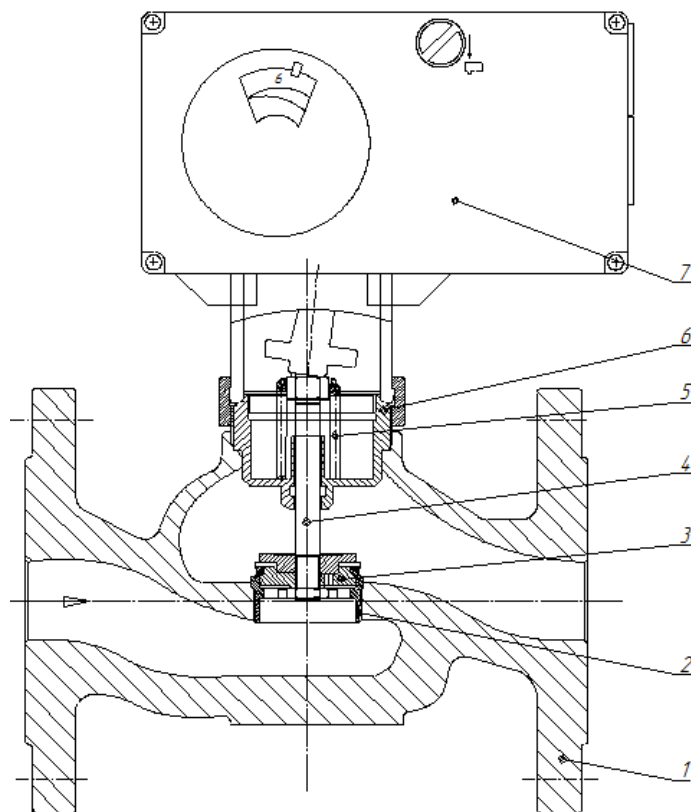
Загальний вид запропонованого електромеханічного водострумний змішувача: 1 – корпус; 2 – сідло клапана; 3 – конус клапана; 4 – шток конуса; 5 – пружина клапана; 6 – направляюча; 7 – сервопривід
